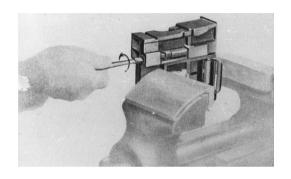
Gesamt-Zerlegung der Waffe: Abschrauben der Führungsstangen für die Zubringerfedern
